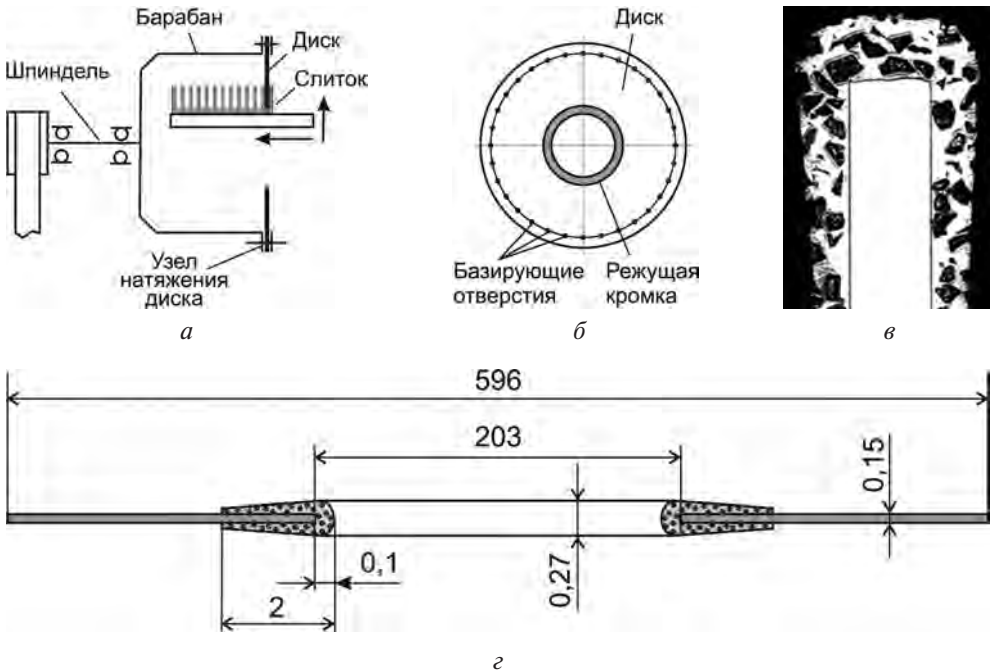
Резка диском с внутренней режущей кромкой:
